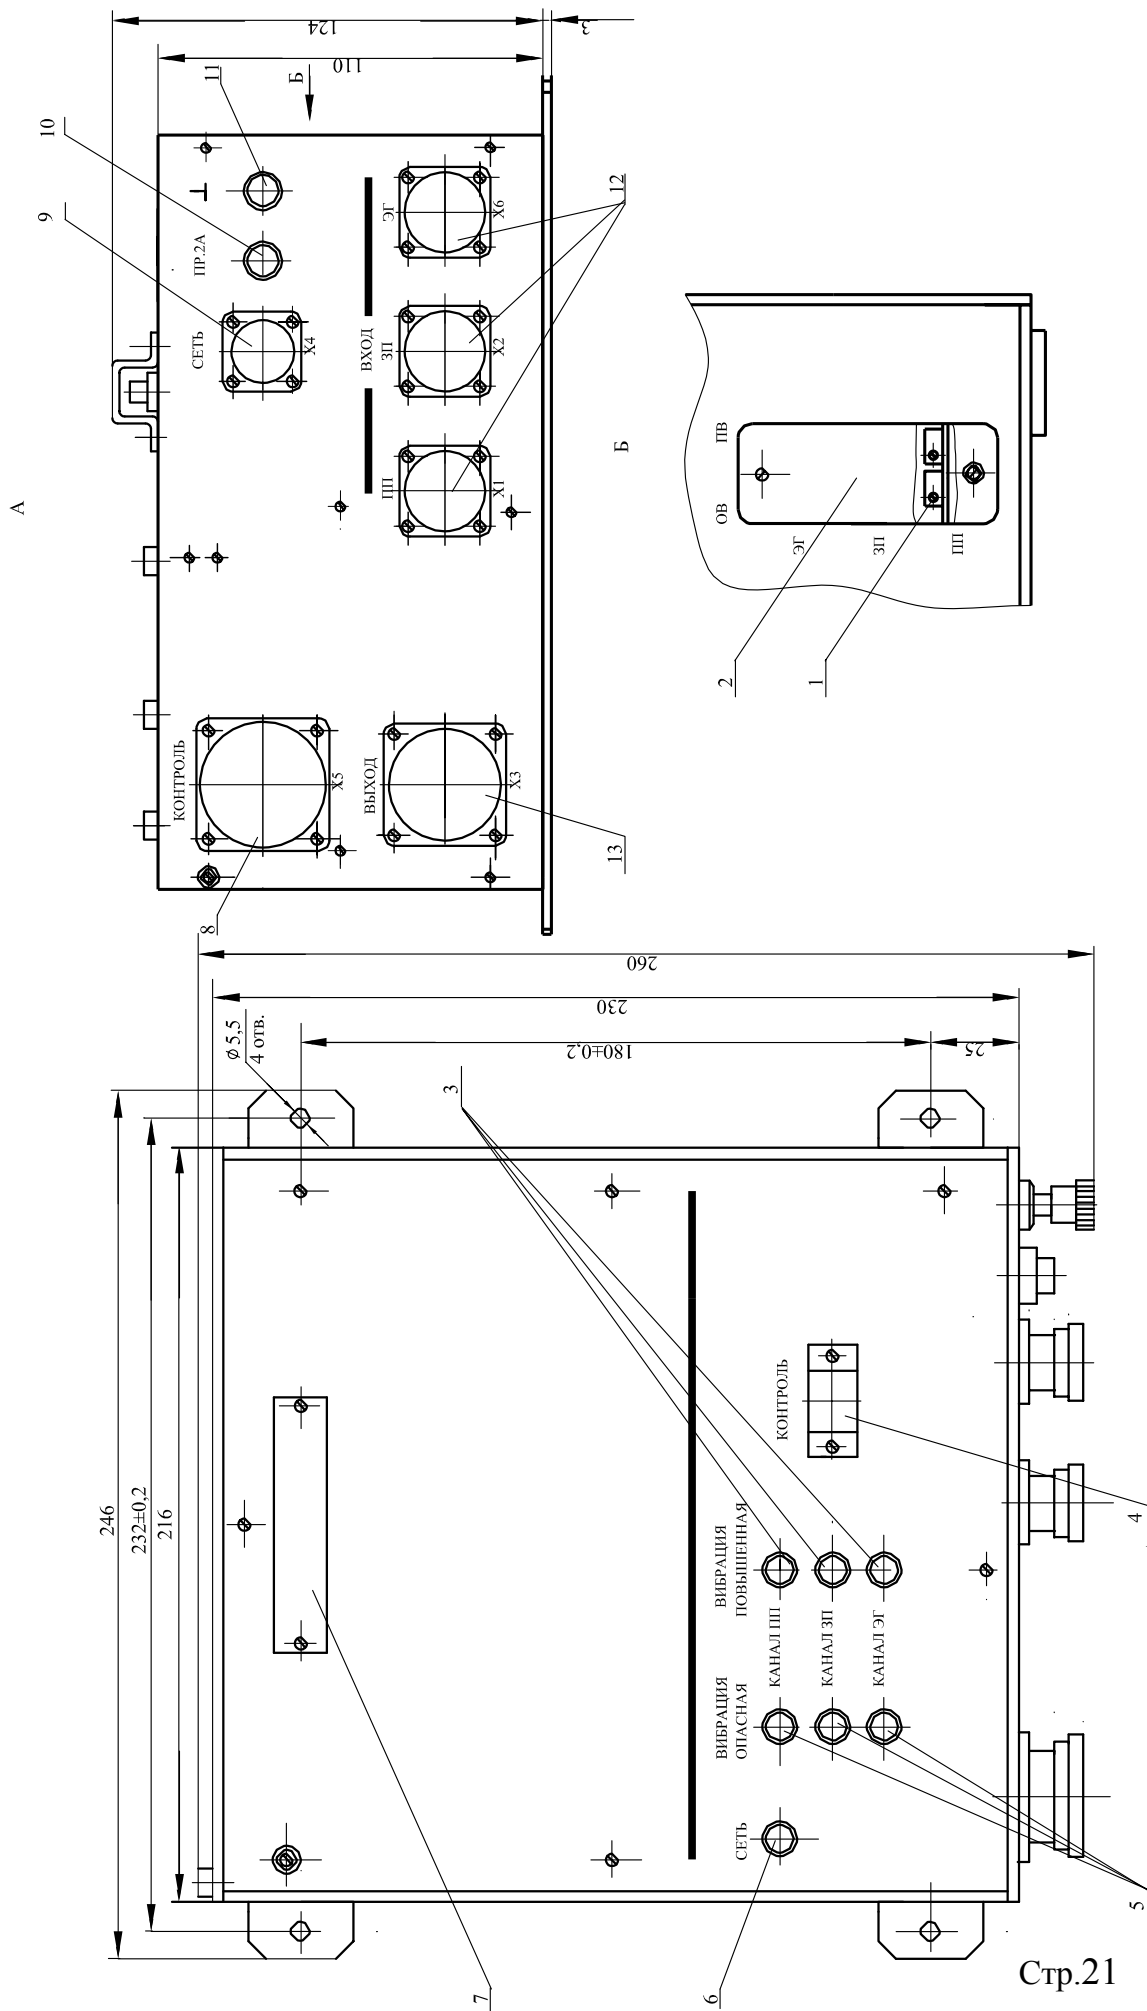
(1 из 2) - Габаритно - установочные размеры блока БЭ - 38 - 13МГ.1
